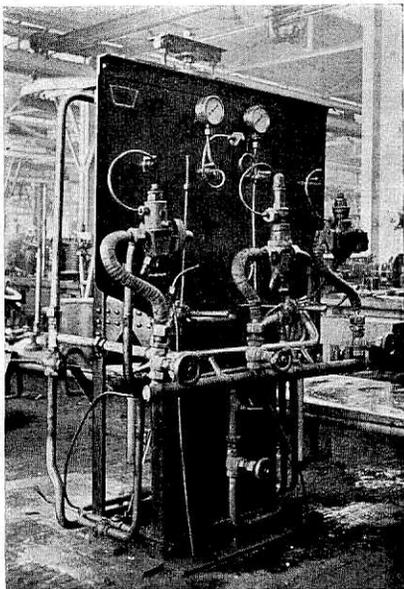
Prüfstand für Luftpumpen-Druckregler.
